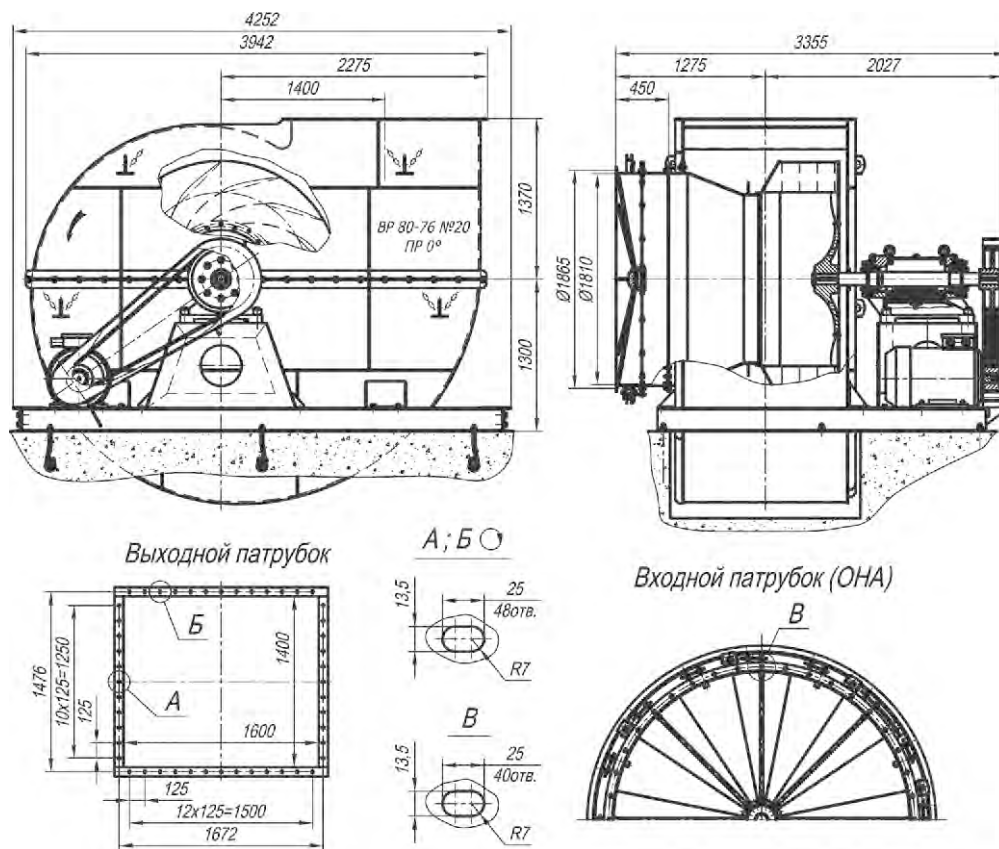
Габаритные и присоединительные размеры вентилятора ВЦ 4-76 (80-76) № 20 исп-5.
